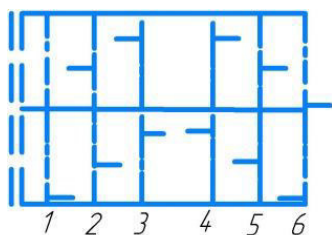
Размещение ножей на развёртке барабана фрезы
